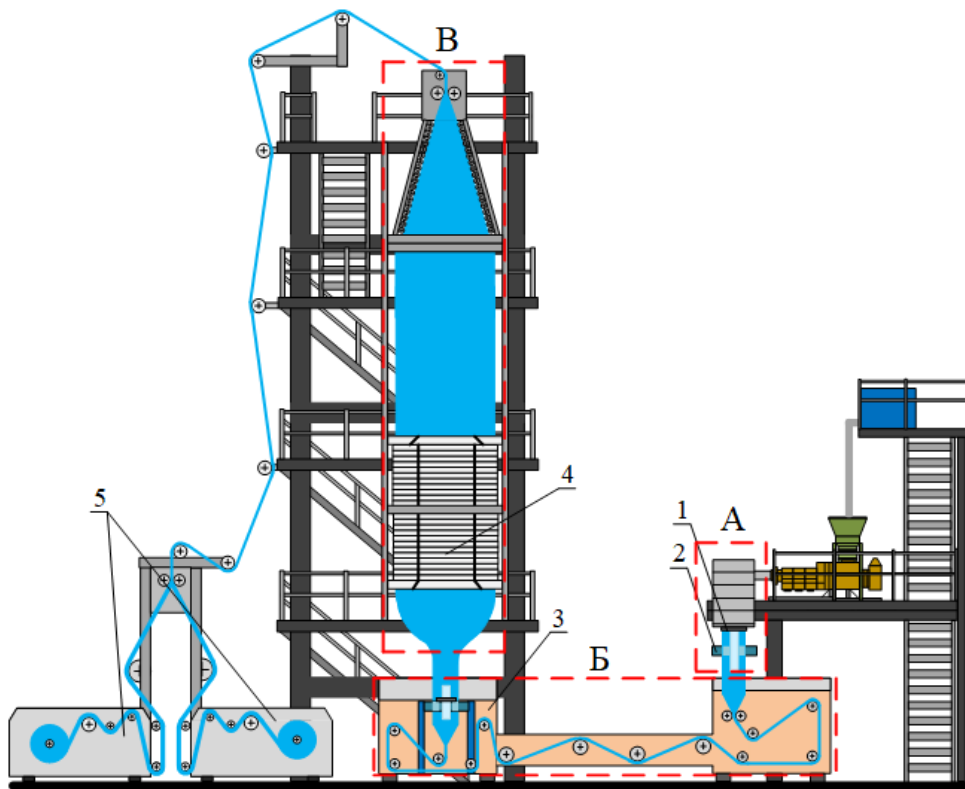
Схема агрегатов для производства термоусадочной пленки из термопластичного полимера рукавным методом. А – зона экструзии расплава и формирования трубчатой заготовки; Б – зона термостатирования заготовки; В – зона раздува заготовки, вытяжки и заделки пленки. 1 – кольцевая фильера; 2 – воздушный компрессор; 3 – резервуар с горячей водой; 4 – контактный холодильник для заделки пленки с полированной металлической поверхностью (кольцевой бандаж); 5 – устройства раскроя рукава и намотки термоусадочной полимерной пленки
